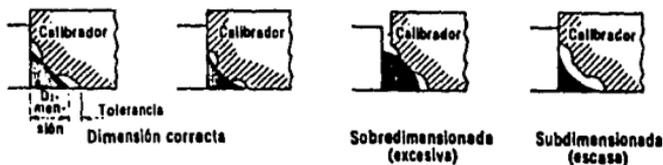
Calibradores para checar el tamaño de soldaduras de filete.
